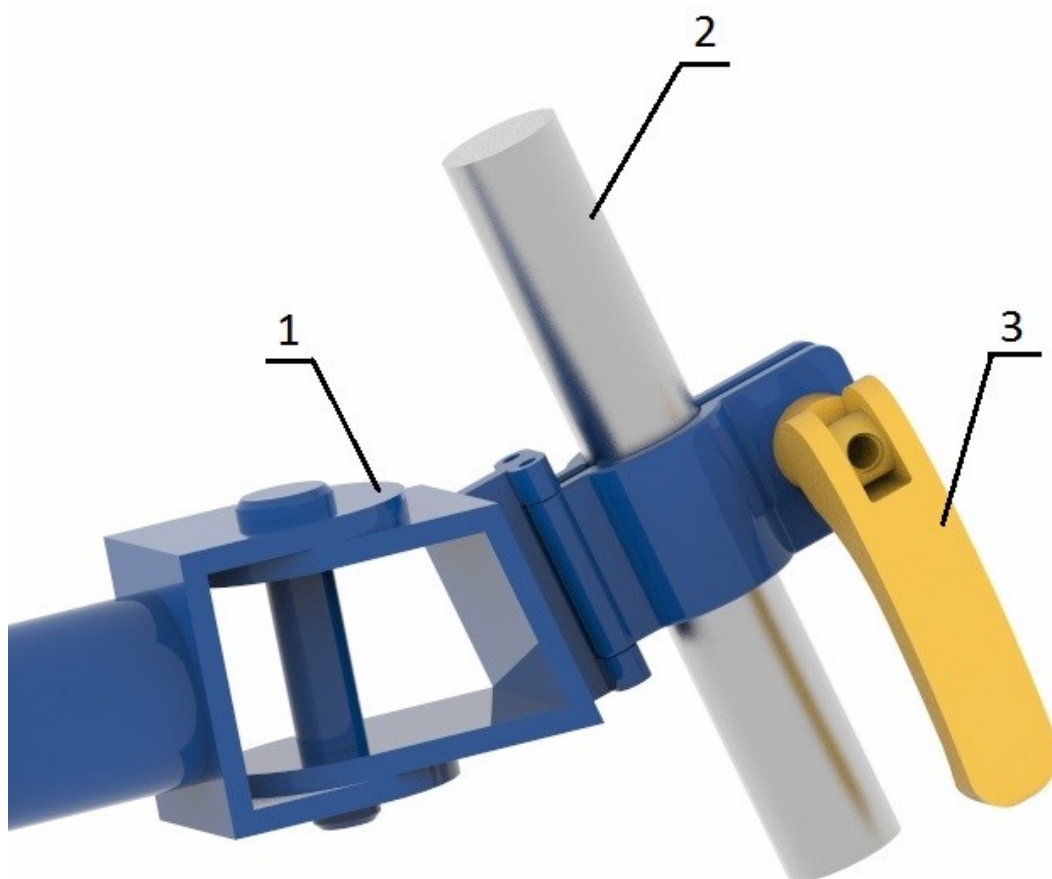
Detail háku bez dětského kola, černě zobrazen záchytný systém (kužel a bočnice), excentrický šroub zobrazen žlutě
